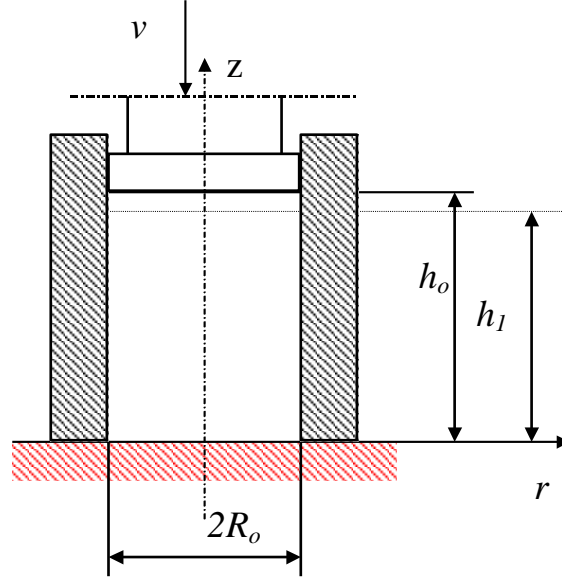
Схема прессования пористой заготовки в закрытом контейнере
